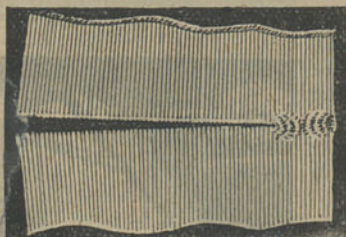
Afastamento em forma de V dos bordos a soldar.
